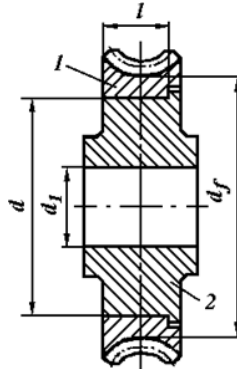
Циліндричне пресове з'єднання вінця черв'ячного колеса з центром
